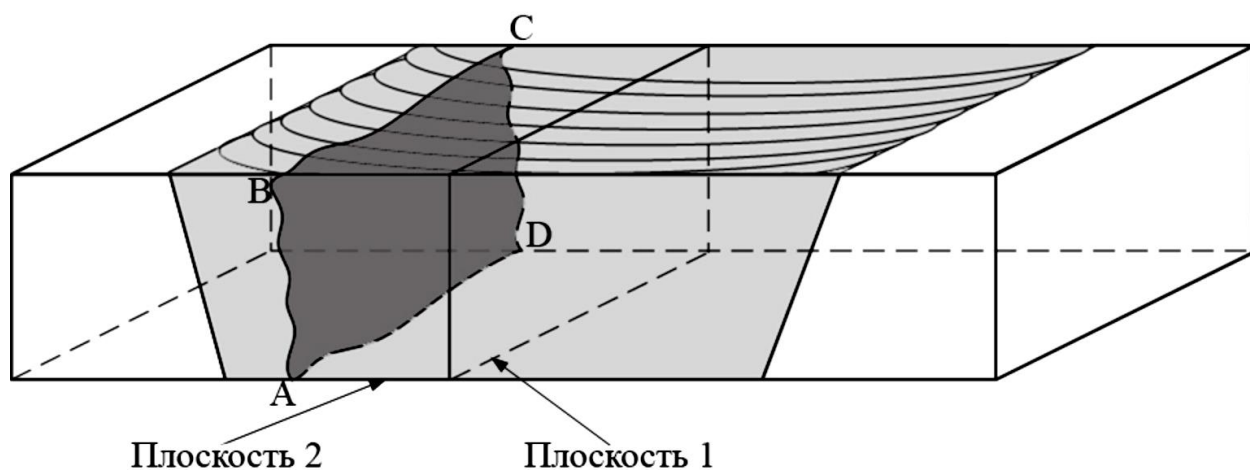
Схема вырезки образцов для исследования структуры сварных соединений: а–в – образцы для металлографических исследований сварных соединений в поперечном сечении; ABCD – область фразтографических исследований
